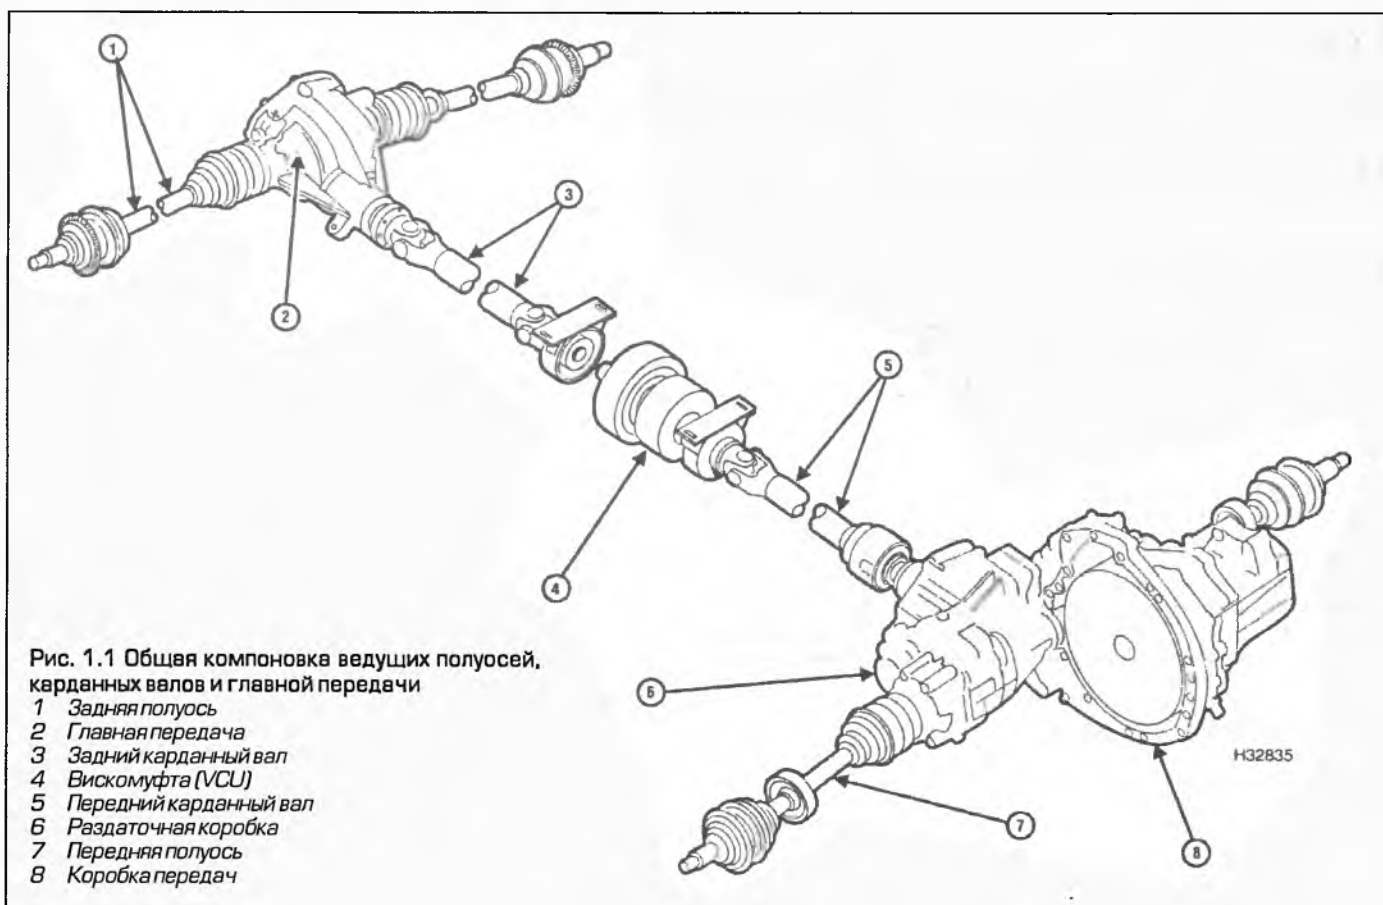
Общая компоновка ведущих полуосей, карданных валов и главной передачи
